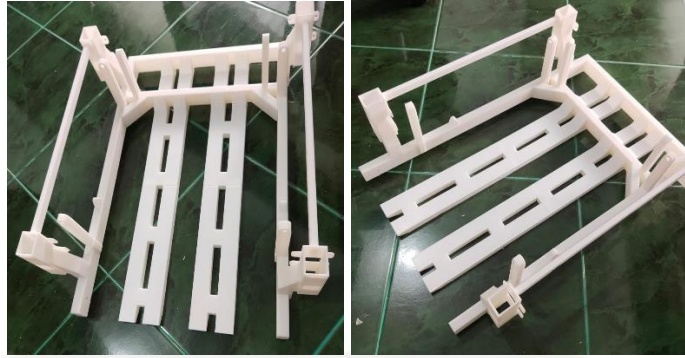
hasil *Assembly Model Rack & Pinion Troli
